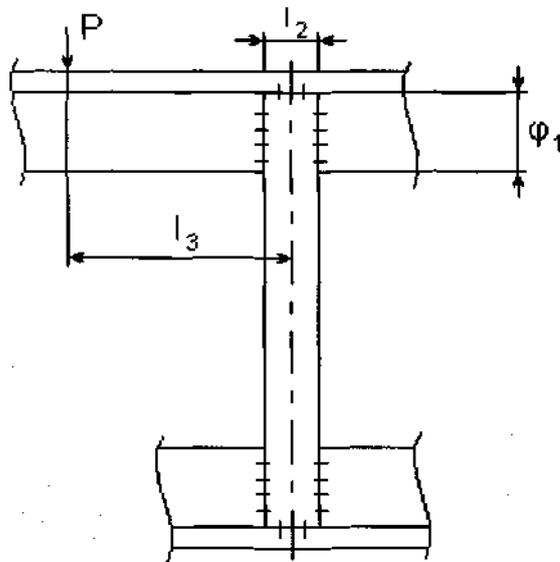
Расчетная схема сварных швов
